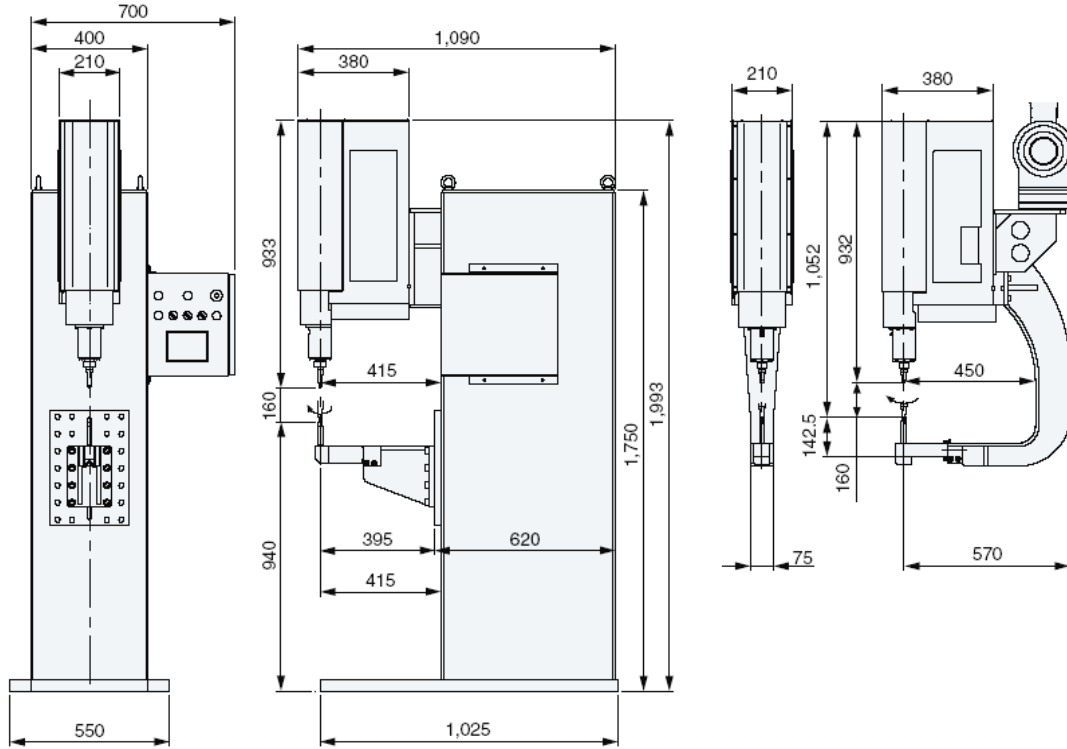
SKNK Robotları (FSSW Robots) [6-8, 22-24]
